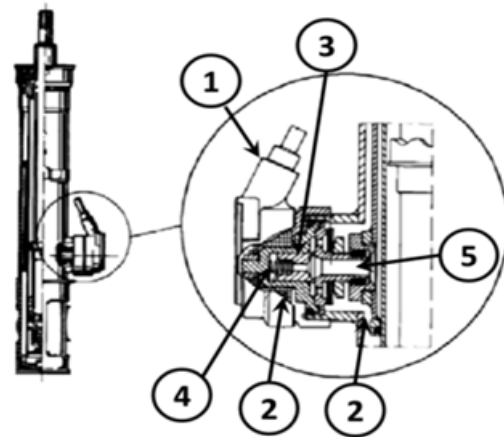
Адаптивний гідро-амортизатор: 1 – корпус; 2 – соленоїд; 3 – якір; 4 – пружина; 5 – електромагнітні клапани
